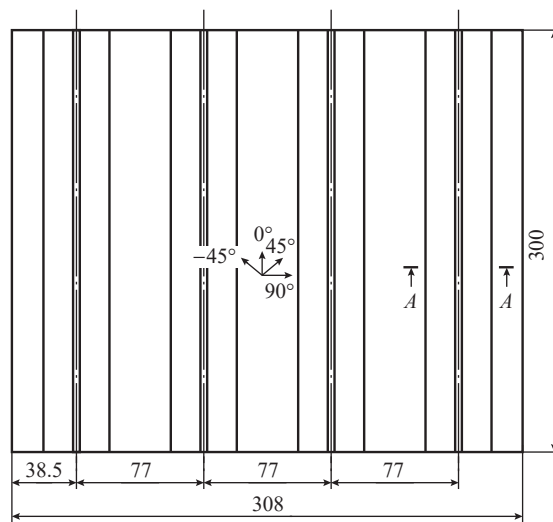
缝合复合材料 T 型加强板平面尺寸 (mm)
